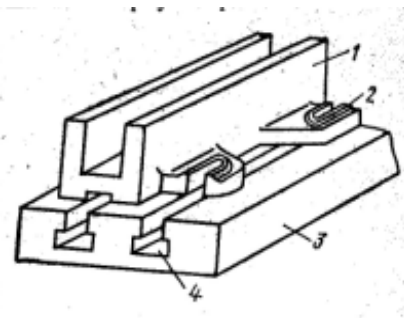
Елементи корпусу для кріплення пристосувань на столі верстата
